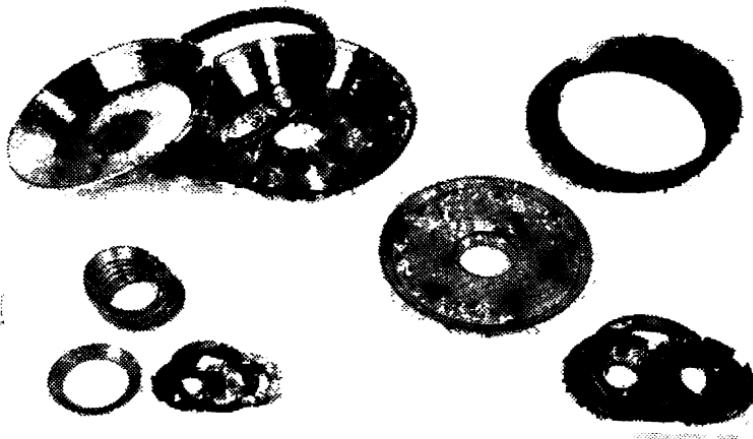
Сборный инструмент из СТМ прогрессивной конструкции
